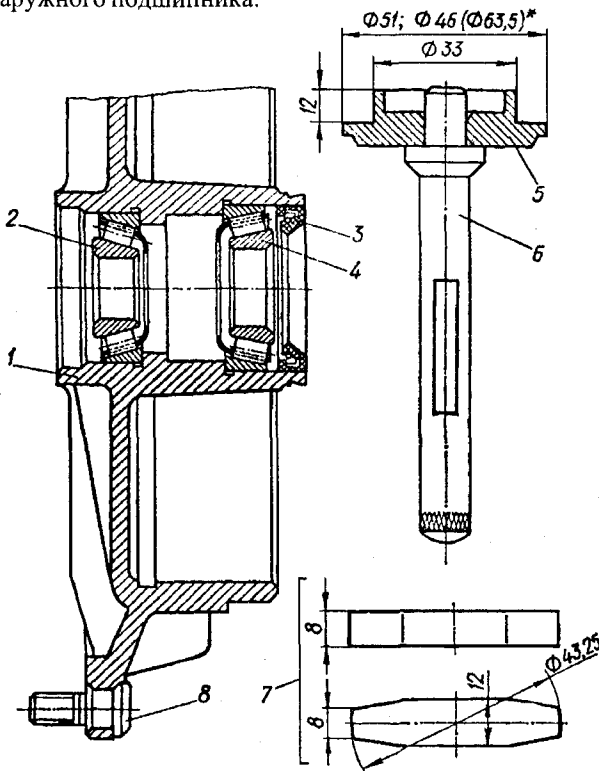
Тормозной барабан заднего колеса в сборе и оправки: 1 – барабан тормозной; 2 – подшипник наружный; 3 – манжета уплотнительная; 4 – подшипник внутренний; 5 – оправка для запрессовки колец подшипников и манжеты; (* – размер $\varnothing 63,5$ мм дан для подшипника ступицы переднего колеса); 6 – ручка оправки; 7 – оправка для выпрессовки наружного кольца внутреннего подшипника; 8 – болт крепления колеса
